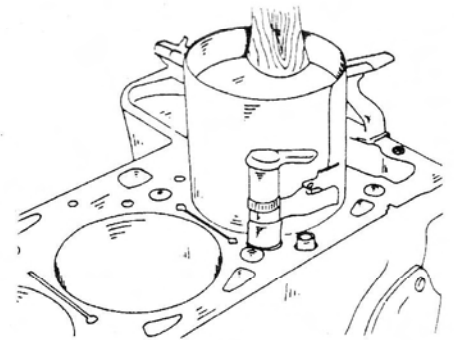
Установка поршня с помощью стяжной ленты поршневых колец.
